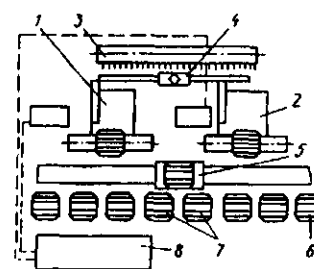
Гибкий автоматизированный участок с двумя модулями и единым автоматизированным загрузочным устройством смены палет и инструмента: 1 и 2 – станки с ЧПУ; 3 – накопитель инструмента; 4 – промышленный робот смены инструмента; 5 – рельсовая тележка-перезагрузчик палет; 6 – палеты для любого станка участка; 7 – позиции загрузки-разгрузки палет; 8 – АСУ распределения загрузки
